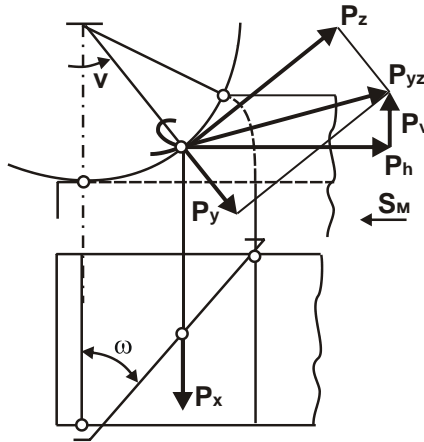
Складові сили різання, які виникають на зубі циліндричної фрези під час зустрічного фрезерування [6]
